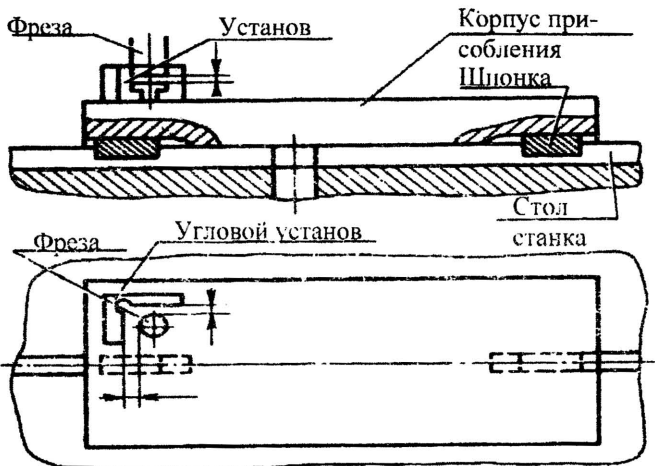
Схемы установки приспособления и заготовки в исходные точки (ИТ) с помощью установа
